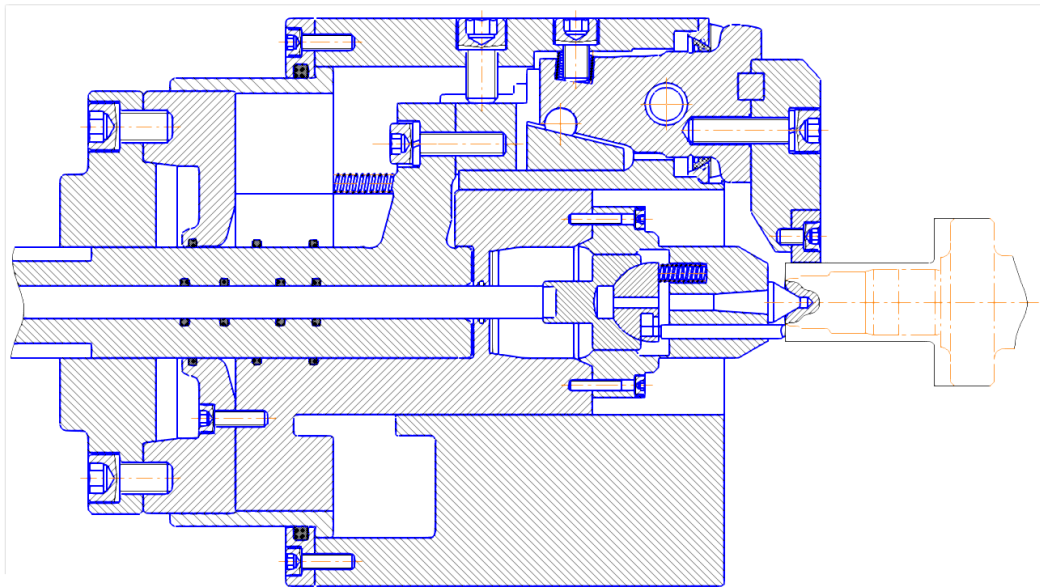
Схема закрепления заготовки в кулачковом патроне с торцеприводом.
